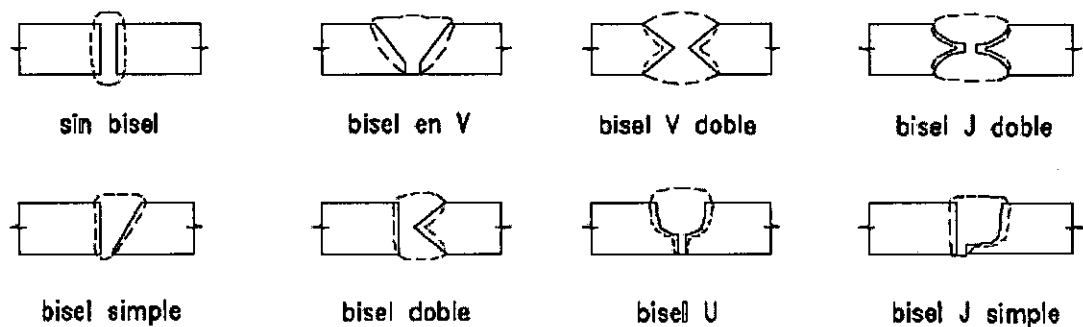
Tipos de Soldadura de Penetración Total
